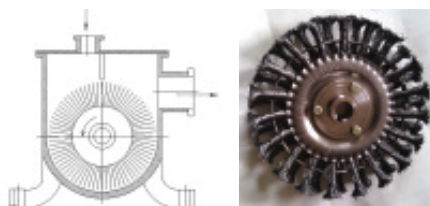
Иглофрезерный измельчитель и его рабочий орган
